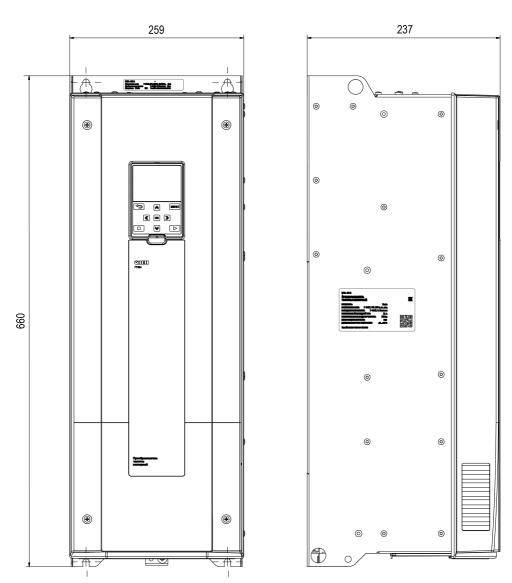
Габаритные размеры прибора в корпусе 4
